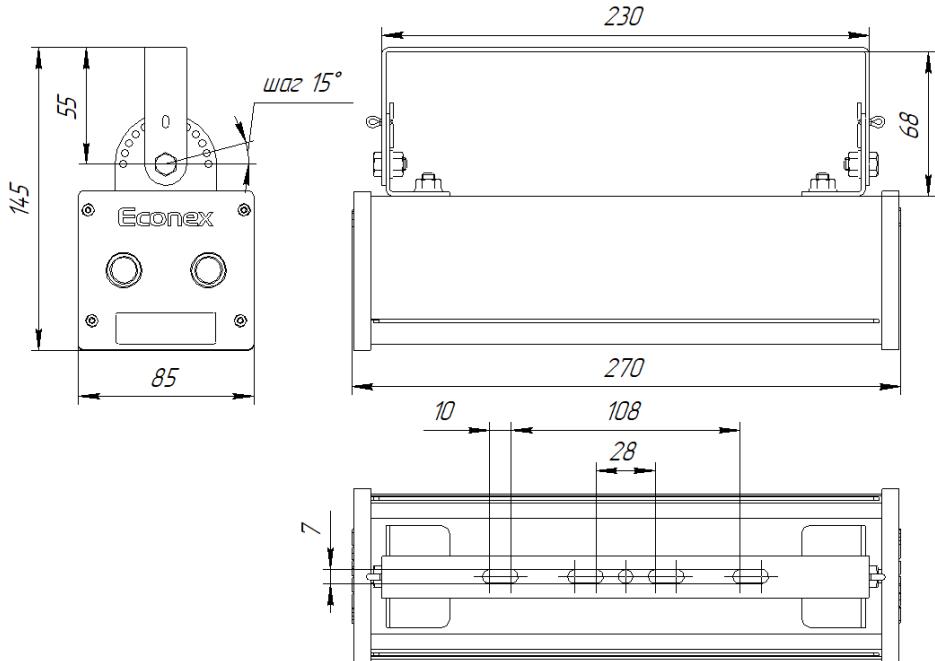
Габаритный чертеж светильника Econex Board G2
